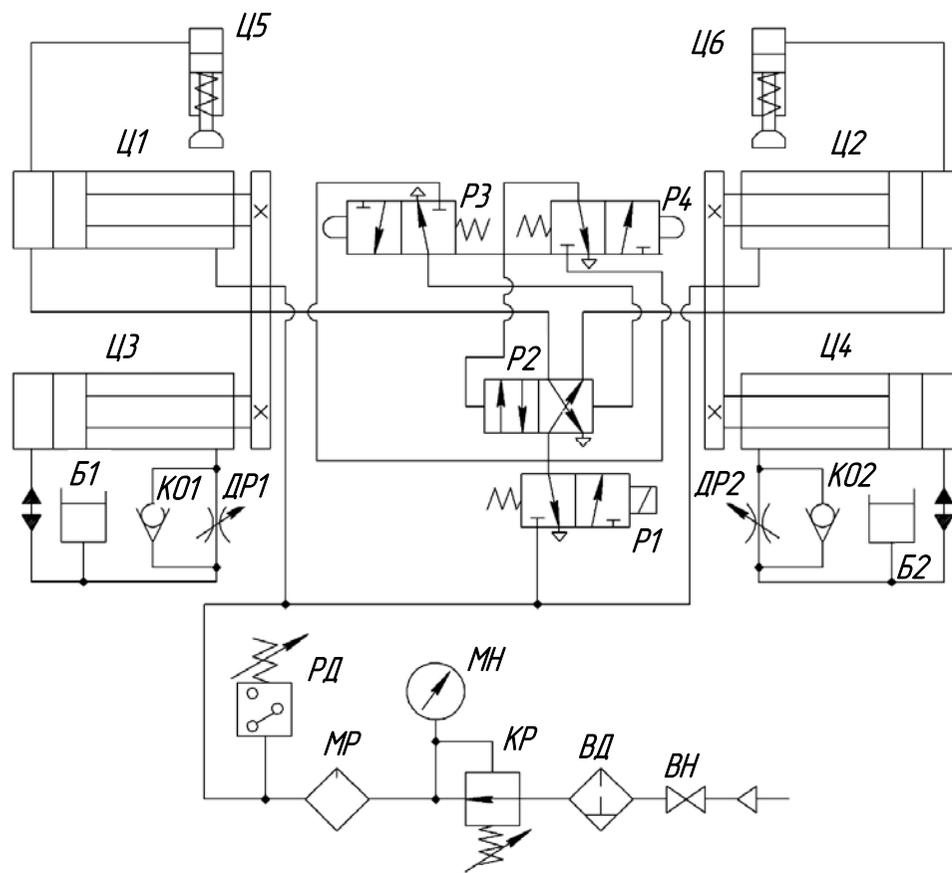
Пневматическая схема сверлильно-пазовального станка СВПГ-2
